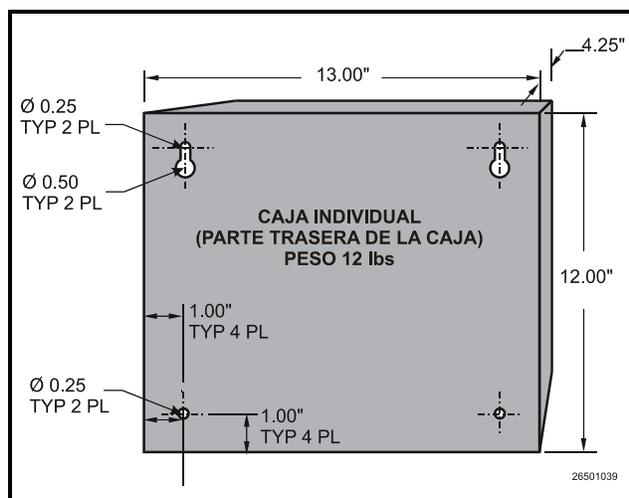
Dimensiones de Montaje de la Caja Individual
